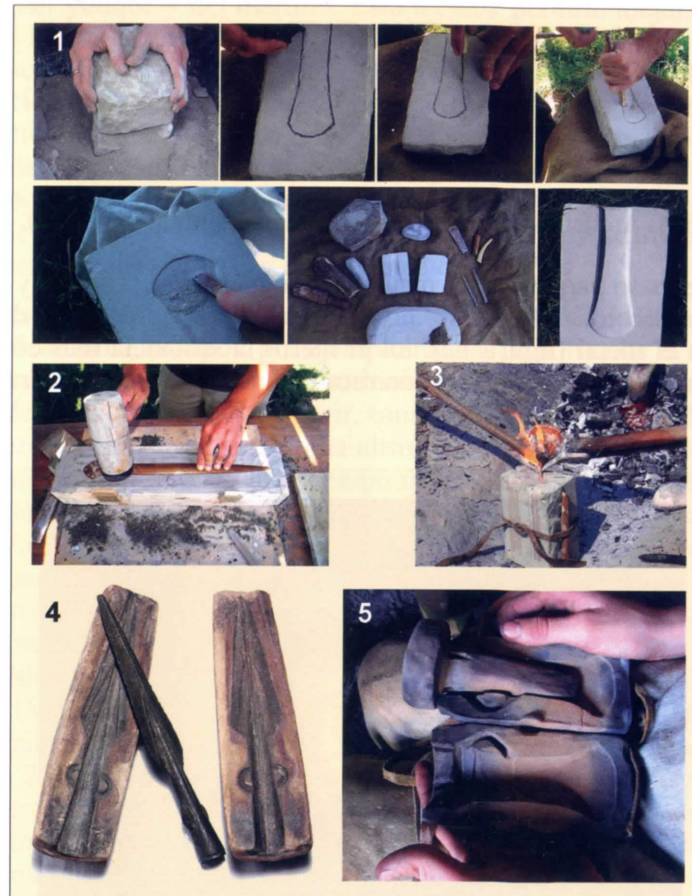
Moldes bivalvos. (1) Fabricación de un molde bivalvo en piedra de un hacha, según Barbieri; (2) Fabricación de un molde bivalvo en arcilla de una espada, según Pellegrini; (3) Vertido del metal líquido en un molde bivalvo; (4) Molde bivalvo de una punta de lanza tubular con dos anillas; (5) Molde bivalvo de un hacha de cubo con el alma para evitar que el metal entre en la zona no deseada.
